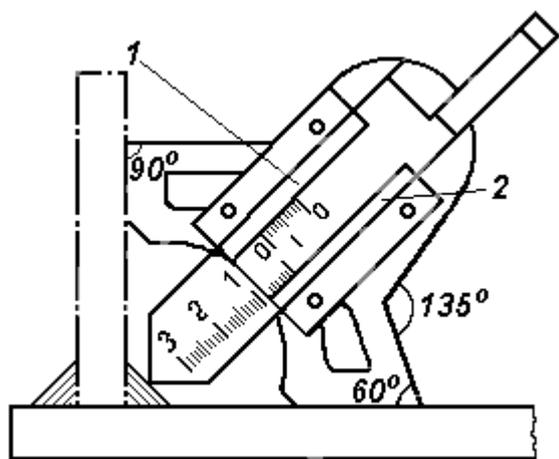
Универсальный измеритель швов: 1, 2 – мерительные линейки
